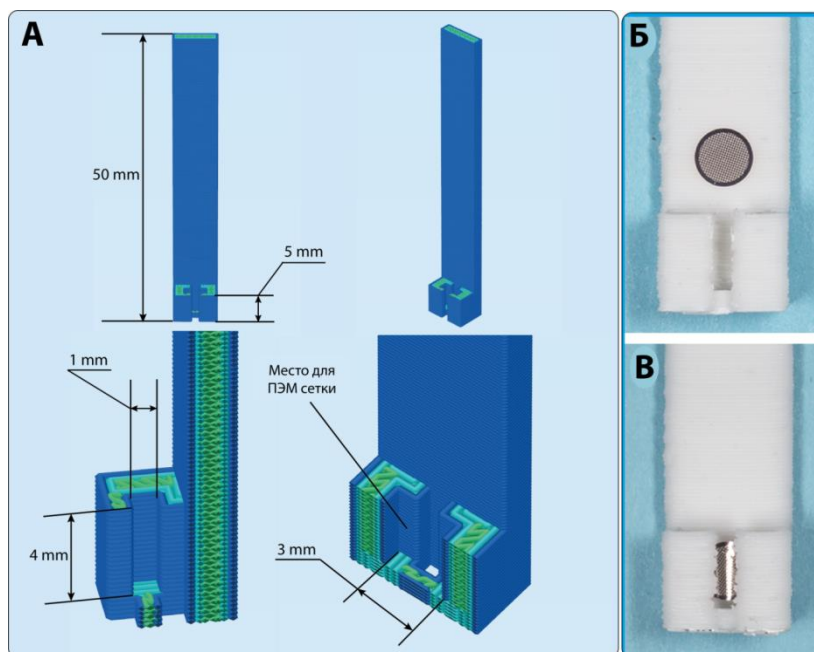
Полипропиленовый держатель, напечатанный с помощью 3D-принтера. Модель и габариты (А), держатель перед загрузкой сетки (Б) и установленная в держатель сетка (В).
